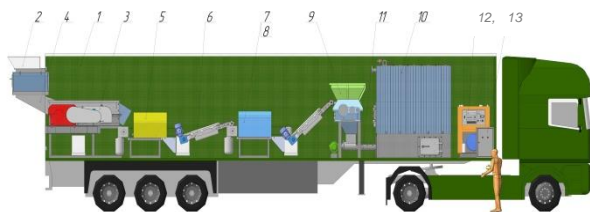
Общий вид мобильной установки. Обозначения: 1 - металлический контейнер, 2 - разрыватель пакетов, 3 - роторный валковый сепаратор, 4 - смежная шахта, 5 - оптикомеханическая сортировка, 6 - ленточный транспортер, 7 - металлоуловитель, 8 - стеклоуловитель, 9 - шредер, 10 - котельный агрегат, 11 - шнековый питатель, 12 - дизель генератор, 13 - щит управления
